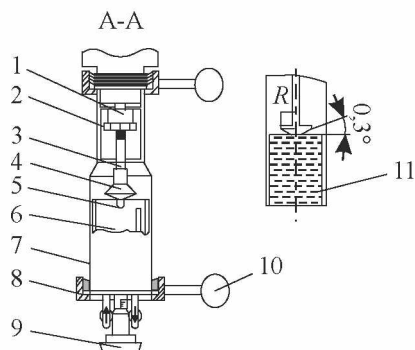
б. Конусно-вимірювальний пристрій: 1 — муфта; 2 — втулка; 3 — вал; 4 — конус; 5 — датчик температури; 6 — термостатична камера; 7 — напрямна пластина; 8 — натяжне кільце; 9 — мікрометричний гвинт; 10 — натяжний важіль; 11 — система конус-пластина
